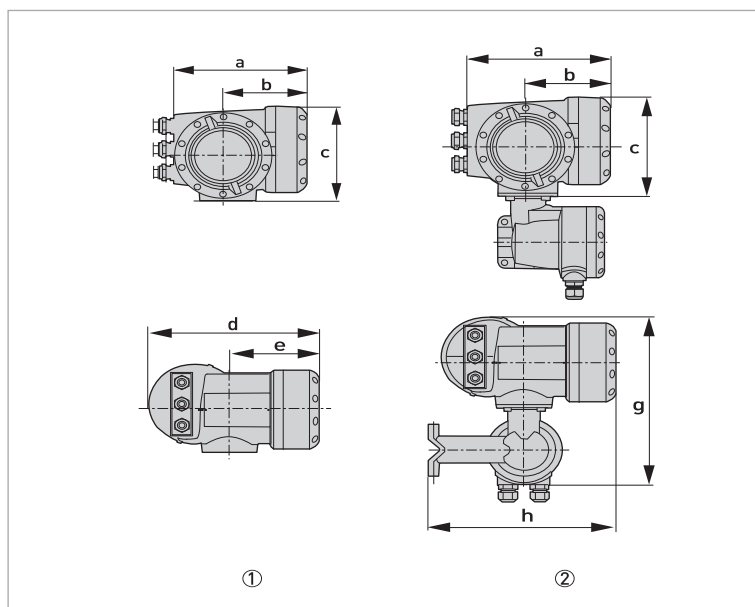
Габаритные размеры корпуса преобразователя сигналов
